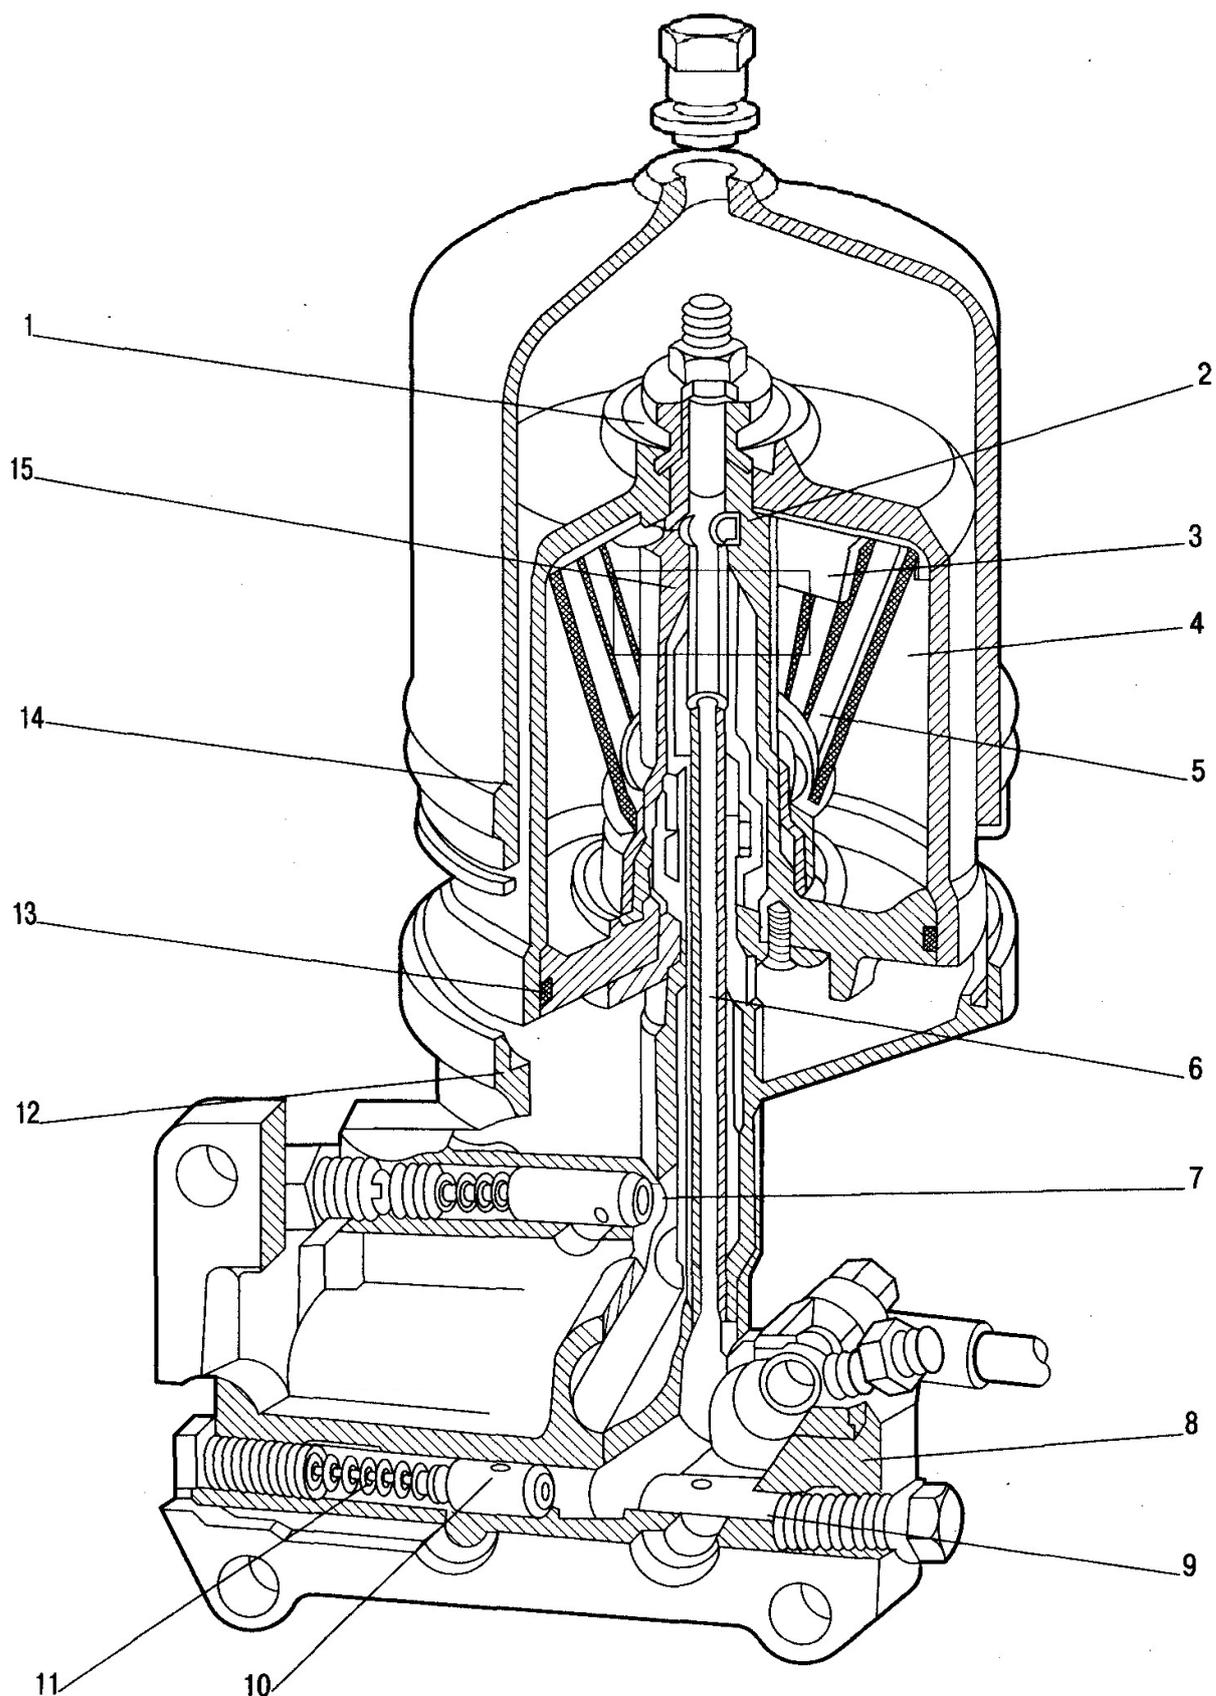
Центробежный масляный фильтр: 1 - гайка; 2 - ось; 3 - прокладка; 4 - стакан; 5 - фильтрующая сетка; 6 - трубка; 7 - предохранительный клапан; 8 - корпус; 9 - сливной клапан; 10 - редукционный клапан; 11 - пружина; 12, 13 - прокладки; 14 - колпак; 15 - корпус ротора
